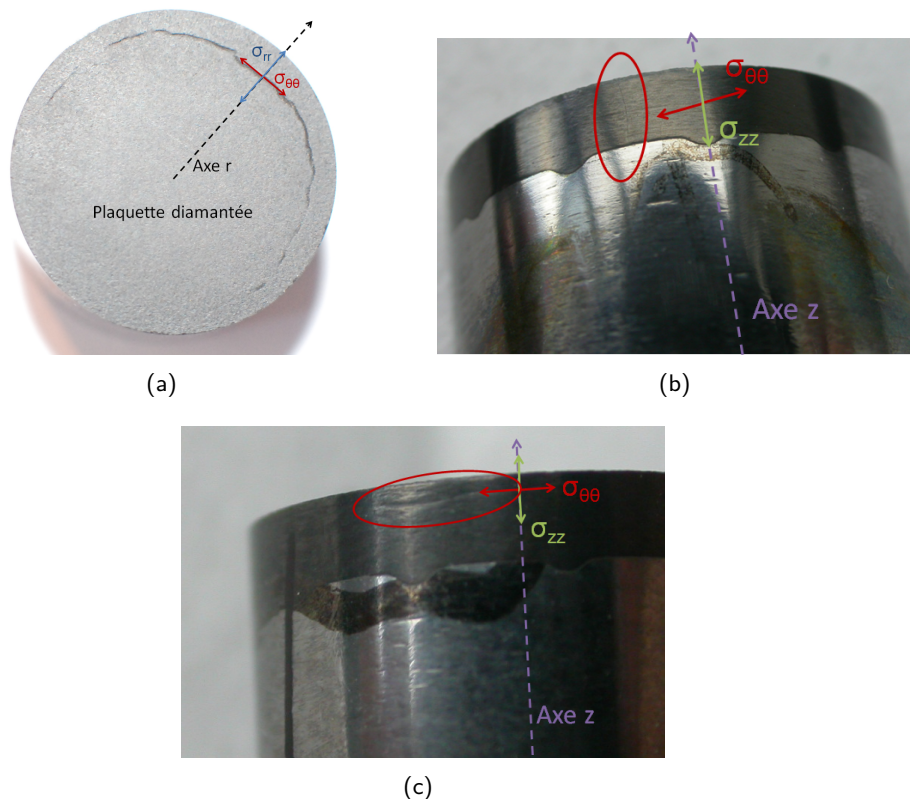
Fissurations pouvant apparaître après assemblage d'un support WC-Co et d'une plaquette diamantée par HPHT (a) circonférentielles ; (b) radiales ; (c) délaminantes
